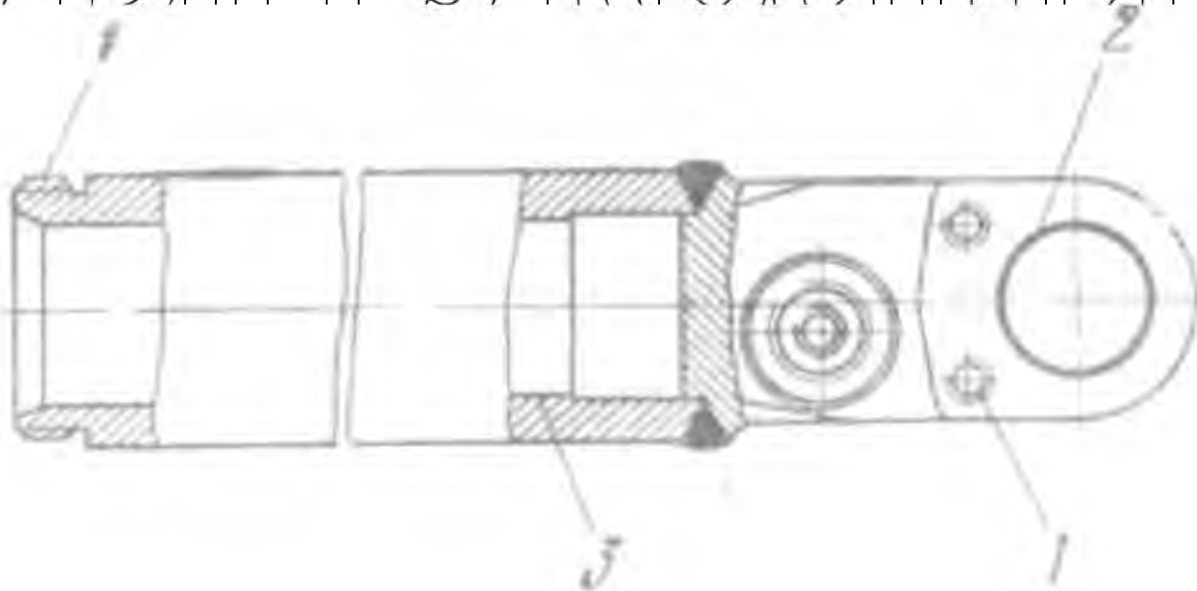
Корпус циліндра в зборі 181.32.015-1
